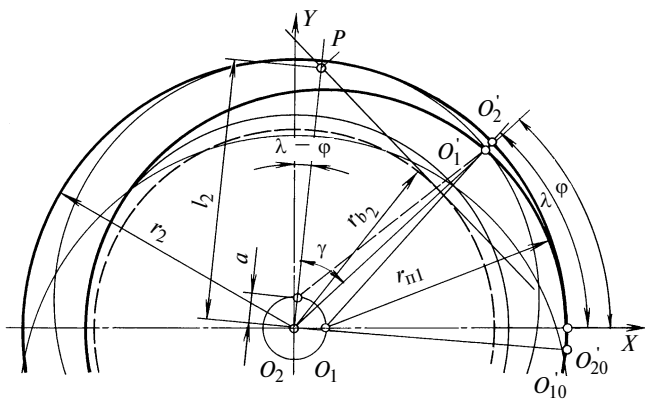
Схема эвольвентного зацепления плунжерной передачи
